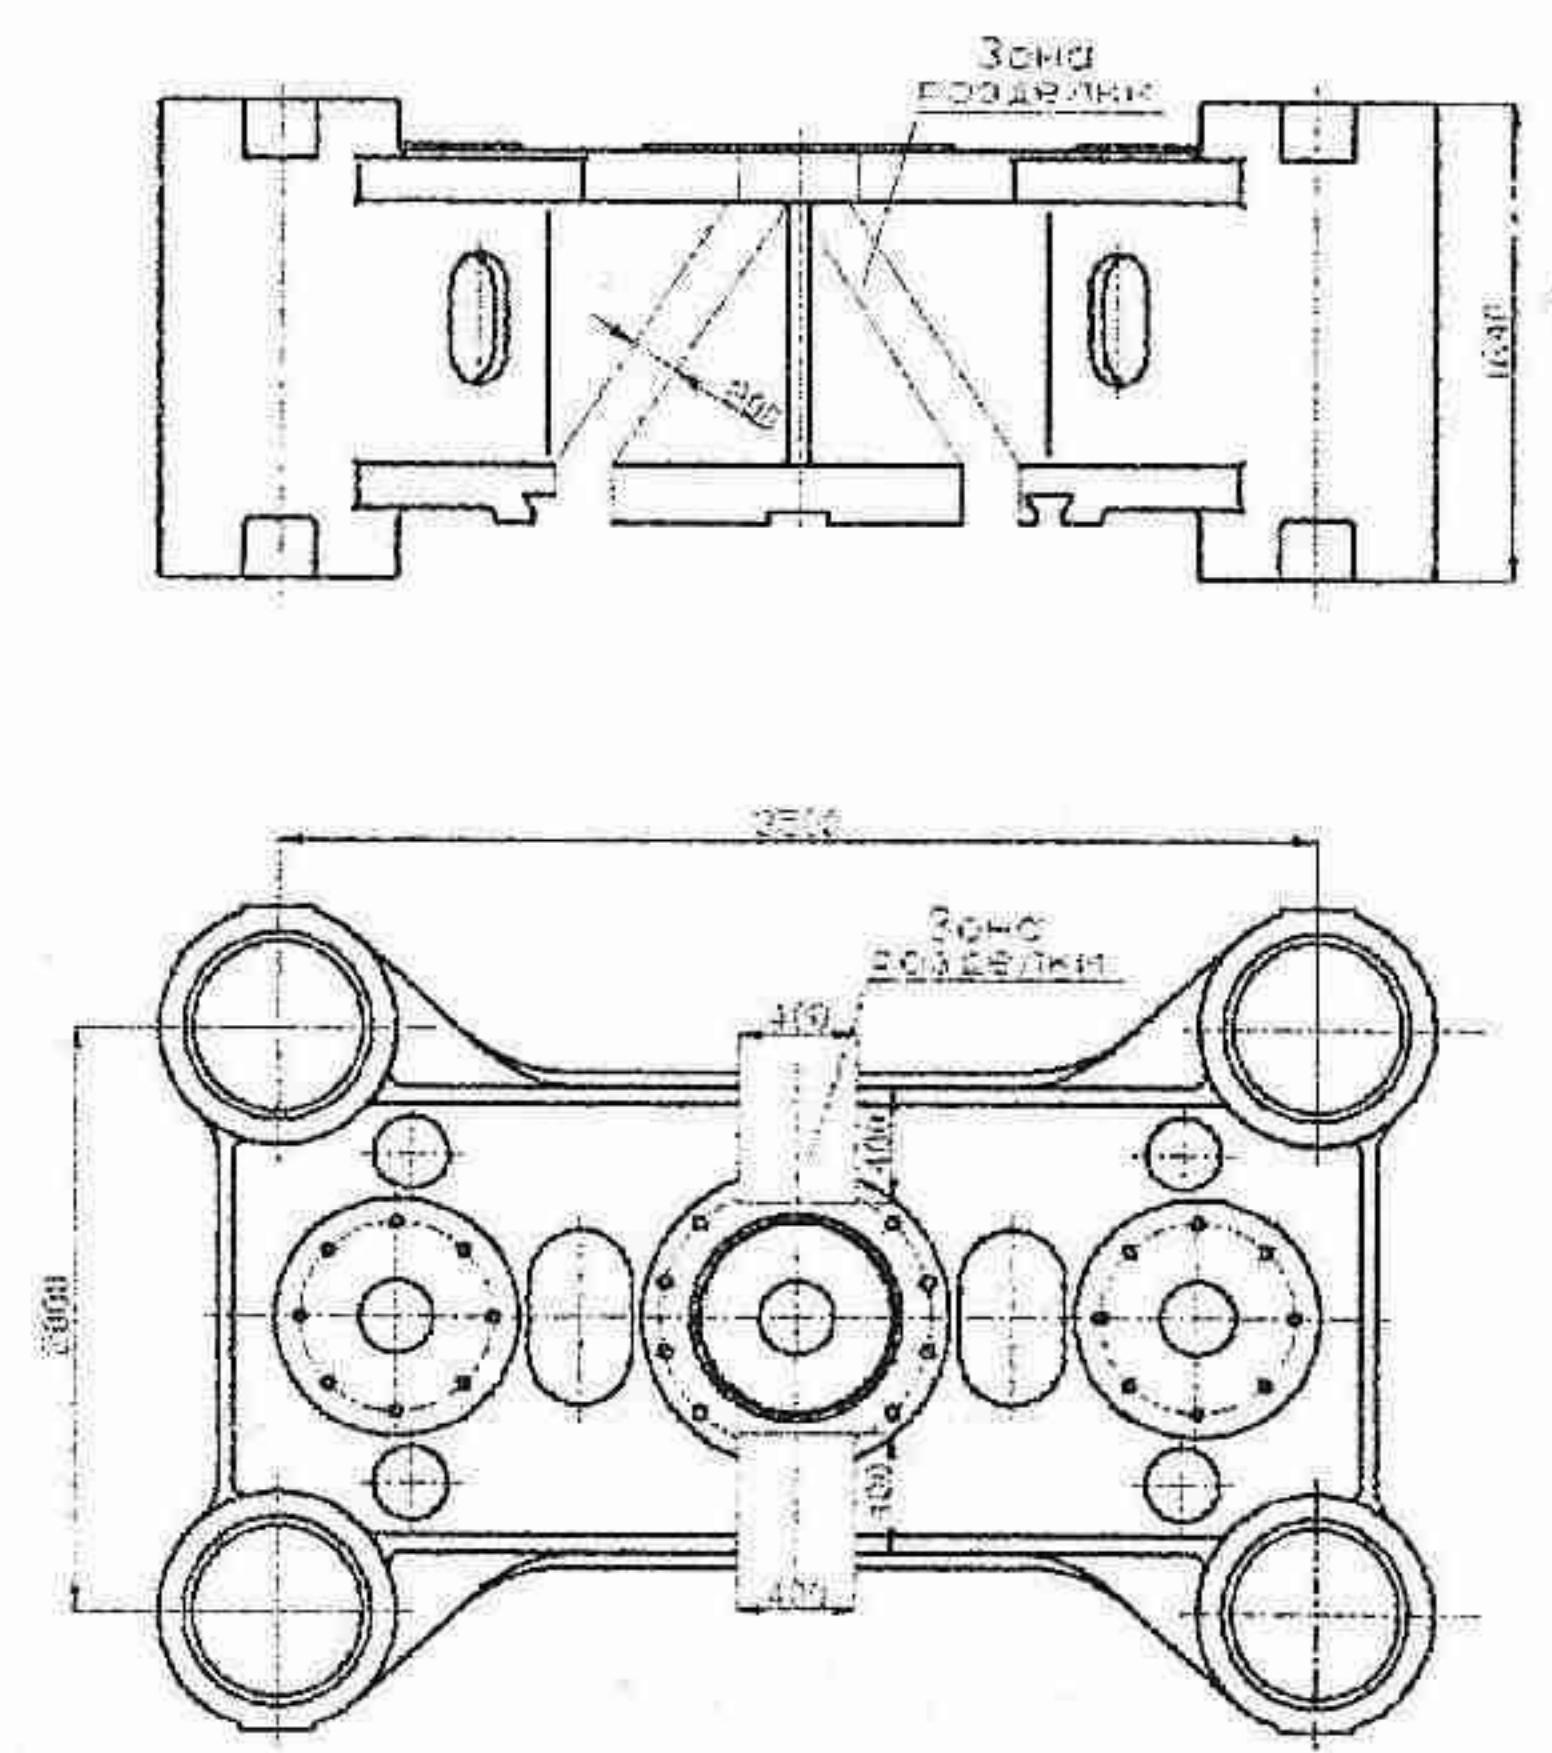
Разделка под сварку боковых стенок, верхнего и нижнего поясов подвижной поперечины ковочного пресса силой 32 МН
